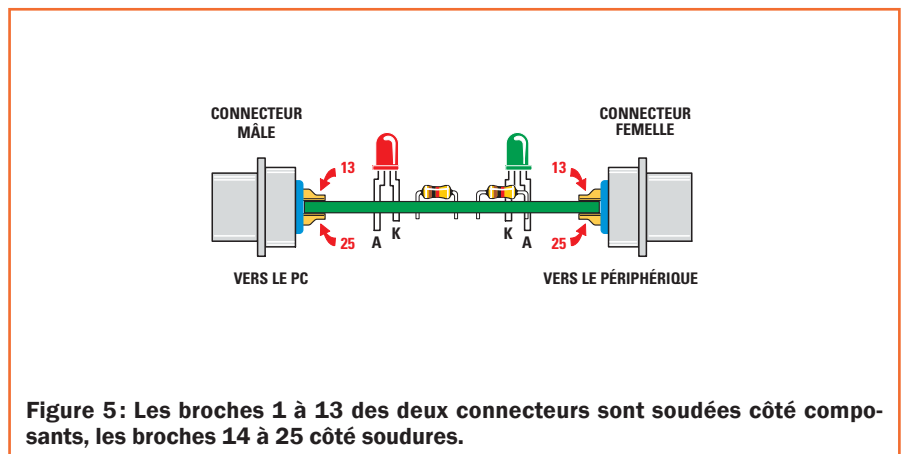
Les broches 1 à 13 des deux connecteurs sont soudées côté composants, les broches 14 à 25 côté soudures.
